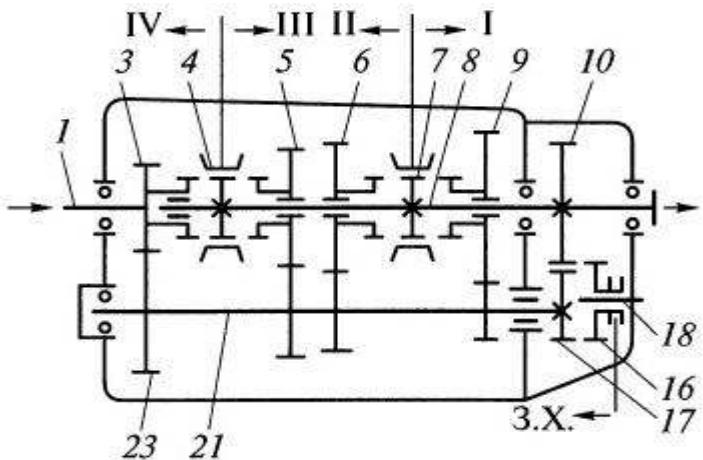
Кинематическая схема трёхвальной коробки передач автомобиля ВАЗ:
